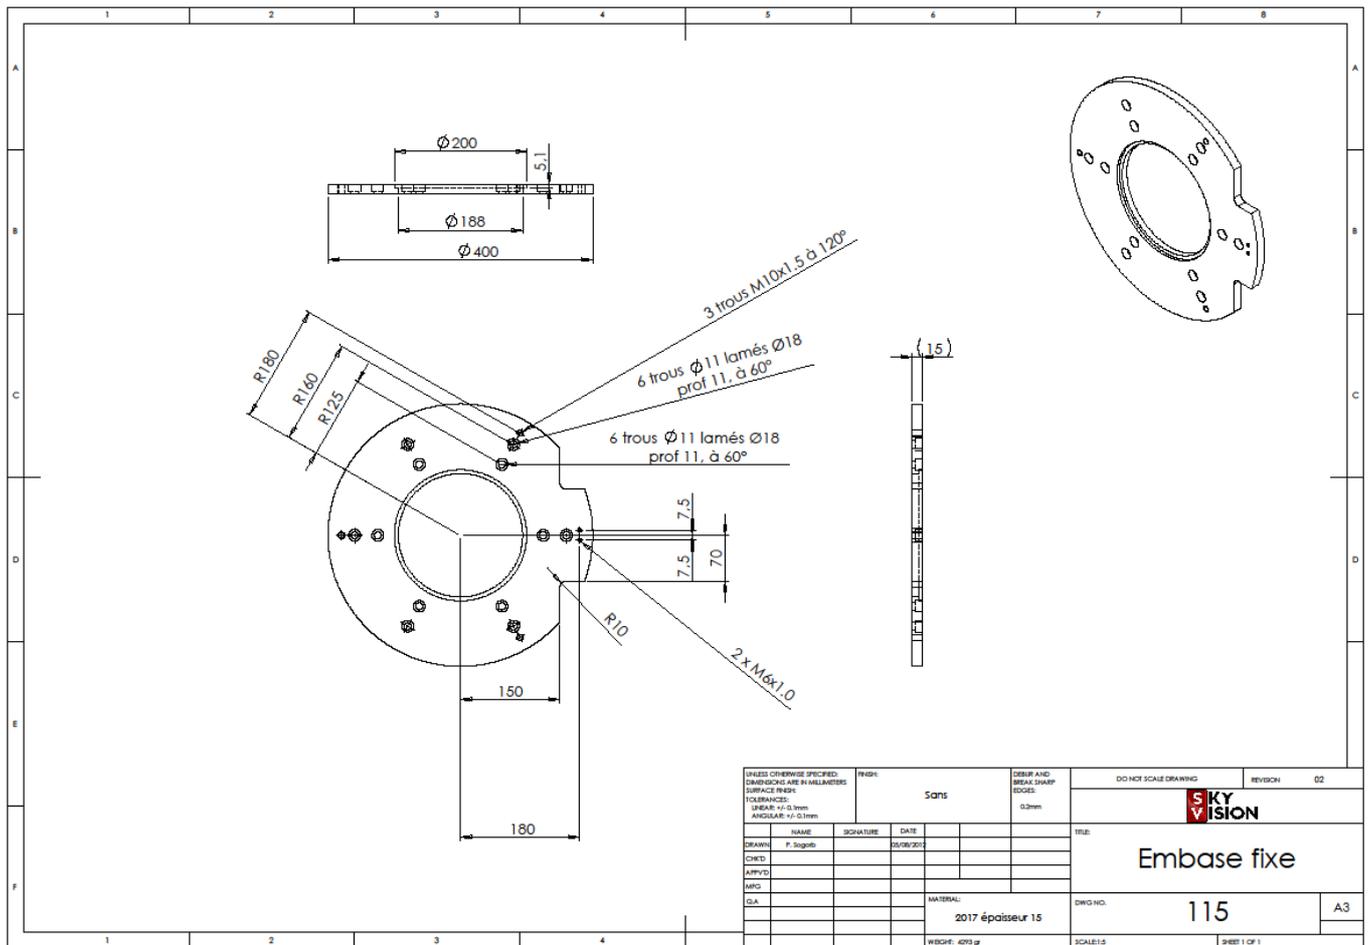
plan de l'interface sur le pied, les trous sur rayon 160 et 125 mm peuvent être utilisés pour fixer la monture à un pied.
